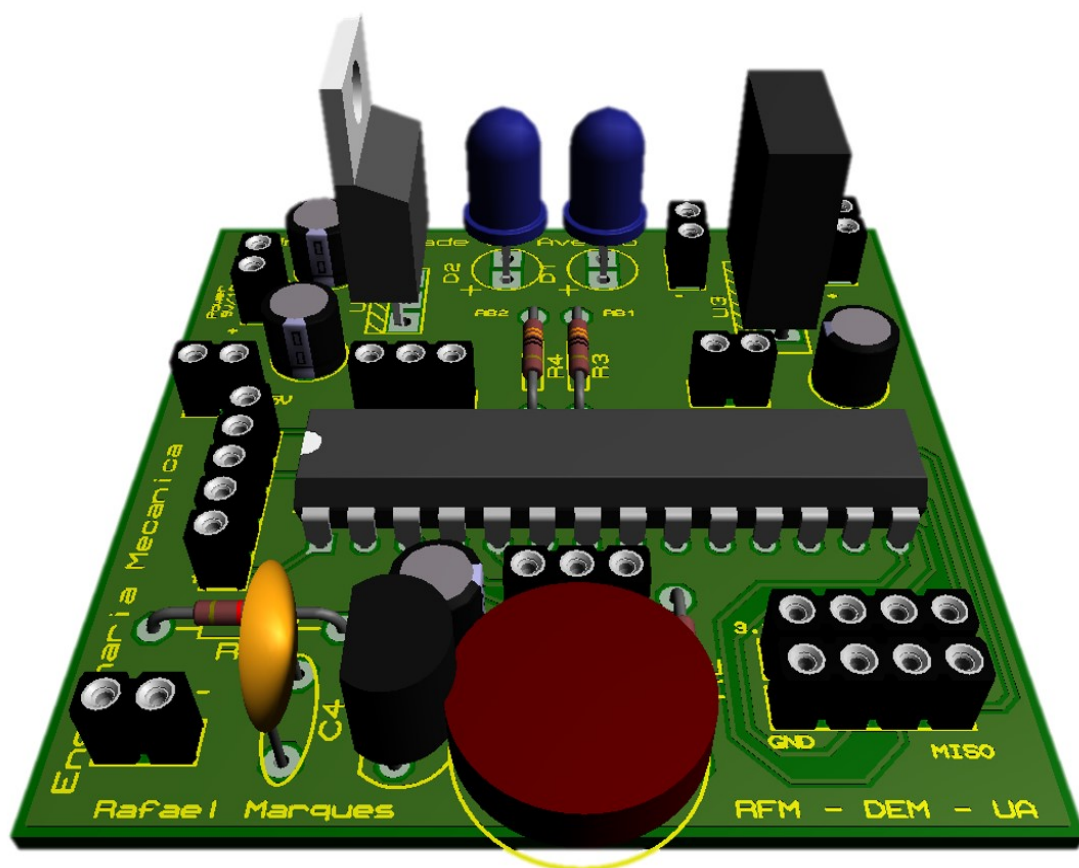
Desenho da PCB e componentes, em 3D - “Módulo reboque”
